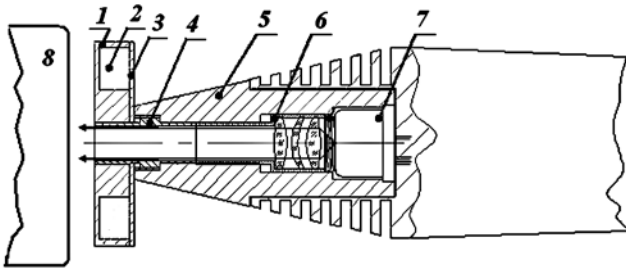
Схема взаимного расположения лазерного излучателя и магнитной насадки в аппарате для магнитолазерной терапии: 1 – корпус магнитной насадки; 2 – кольцевой магнит; 3 – сердечник из магнитомягкого материала в виде пластины с отверстием, расположенной на поверхности магнита со стороны, обращенной к лазерному диоду; 4 – сердечник в виде трубки, расположенной вдоль оси магнита; 5 – корпус лазерного излучателя; 6 – коллиматор для формирования лазерного луча с заданной расходимостью; 7 – лазерный диод; 8 – объект воздействия
